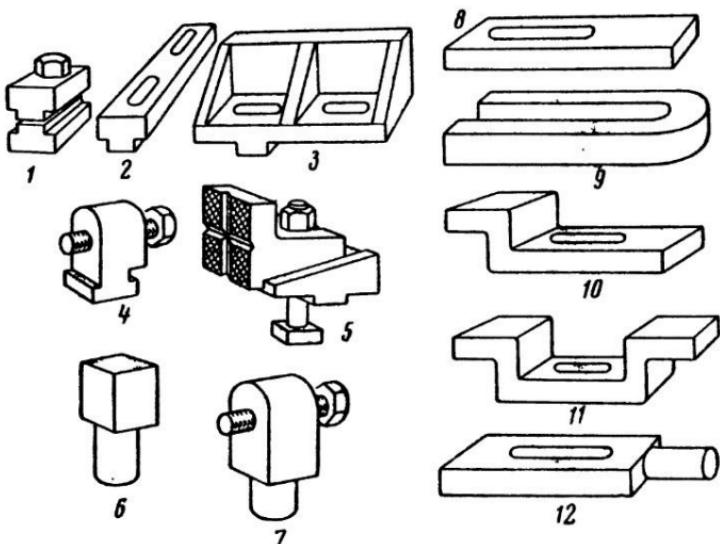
Приспособление для крепления деталей на строгальном станке: 1 — упорная колодка; 2 — упорная планка; 3 — упорный угольник; 4 и 5 — прижимные колодки для крепления деталей на столе станка с Т-образным пазом; 6 и 7 — упор и прижимная колодка для крепления на столе станка деталей с цилиндрическими отверстиями; 8—12 — прихваты различной конструкции.
